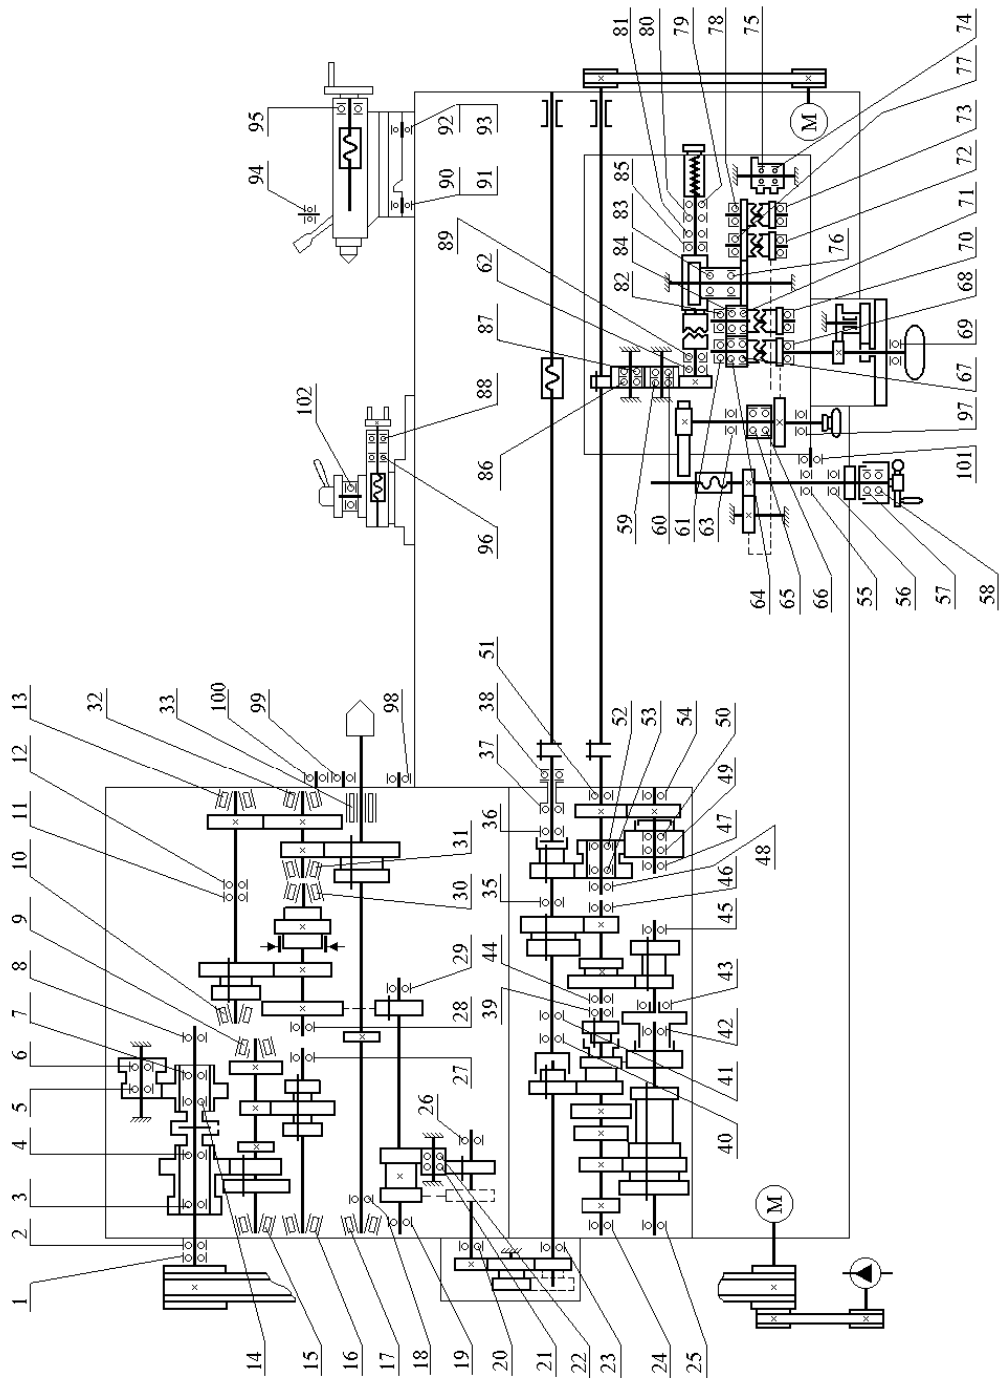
Схема расположения подшипников станка 16B20, 1B62Г
